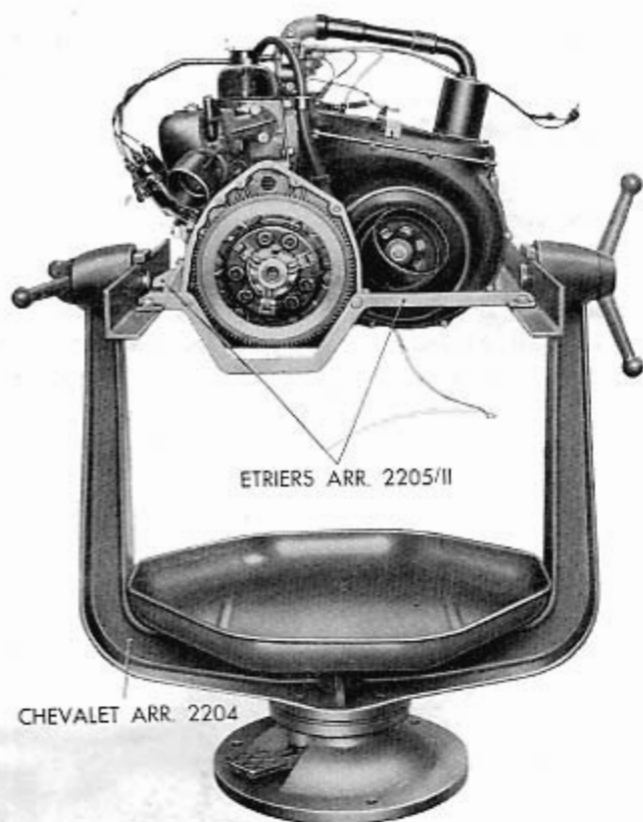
Moteur sur le chevalet rotatif Arr. 2204 fixé par les étriers Arr. 2205/II.
